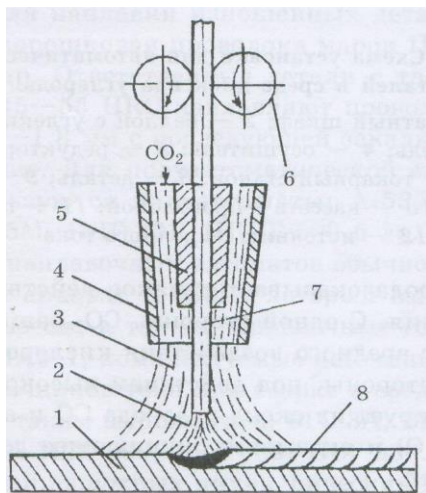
Схема дуговой сварки в среде диоксида углерода
